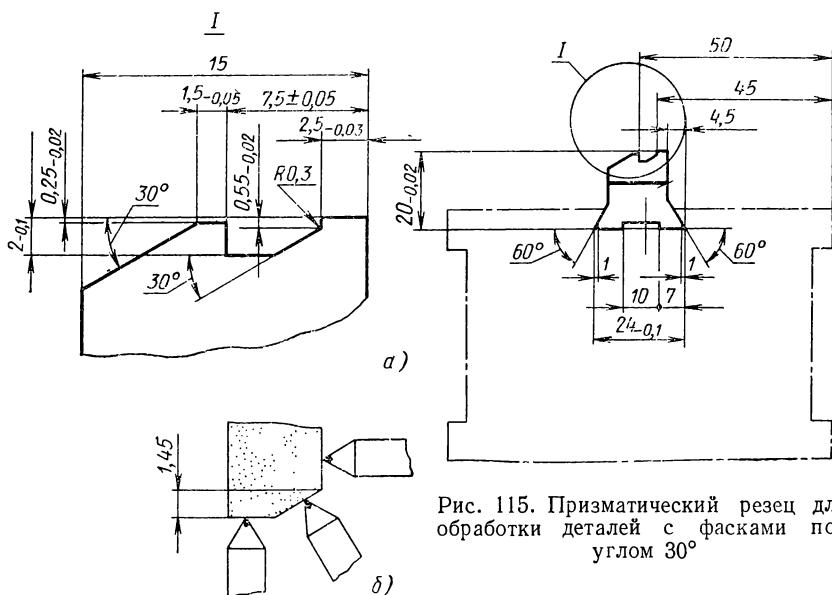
Призматический резец для обработки деталей с фасками под углом 30°
